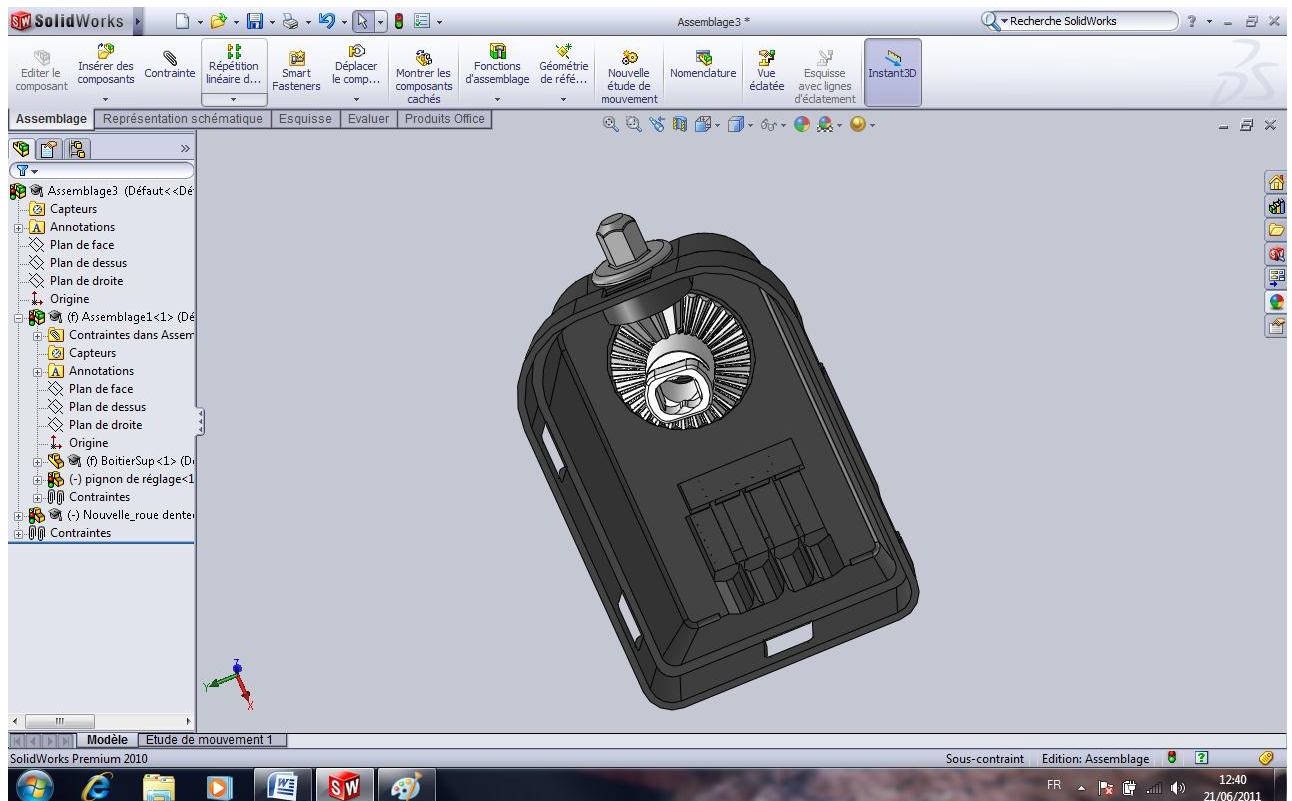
Assemblage 2 (assemblage 1 +roue dentée de renvoi)
